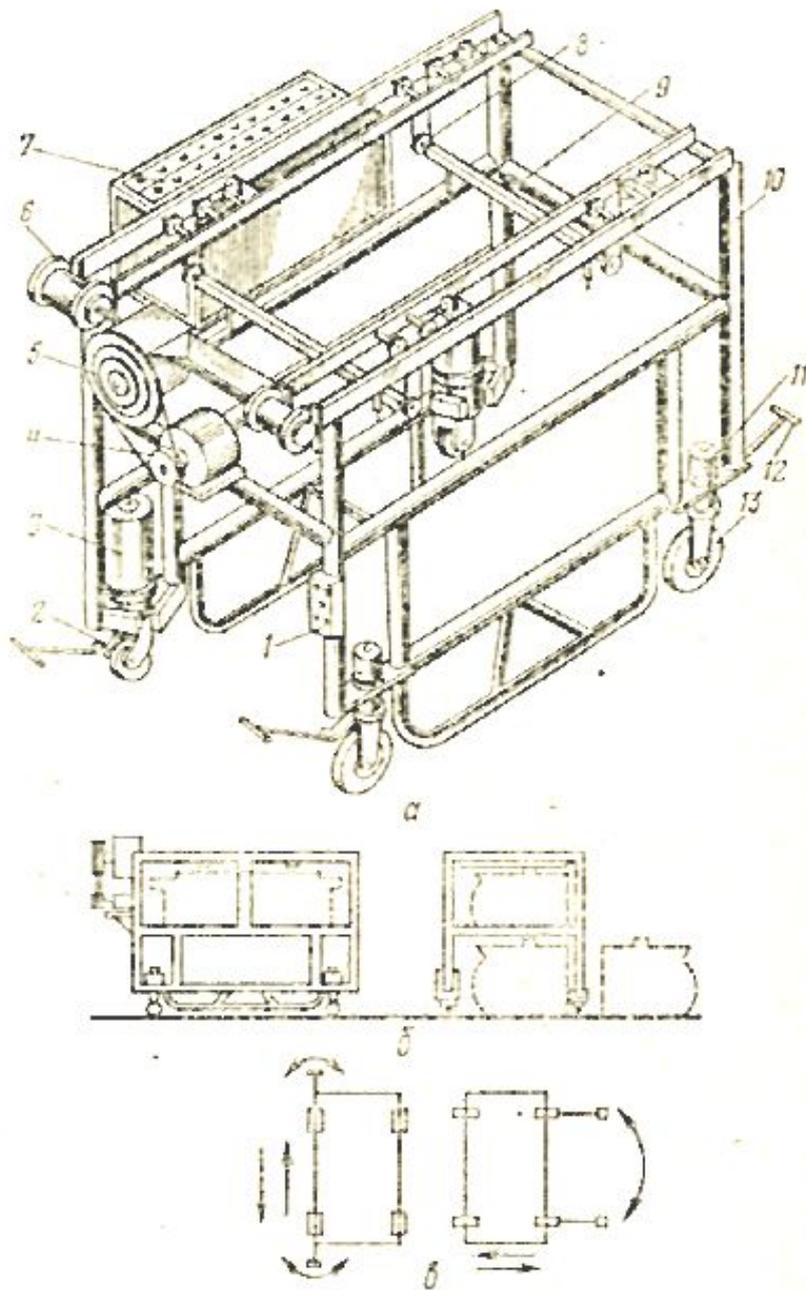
Подъемно-транспортное устройство для станка АТПР:
